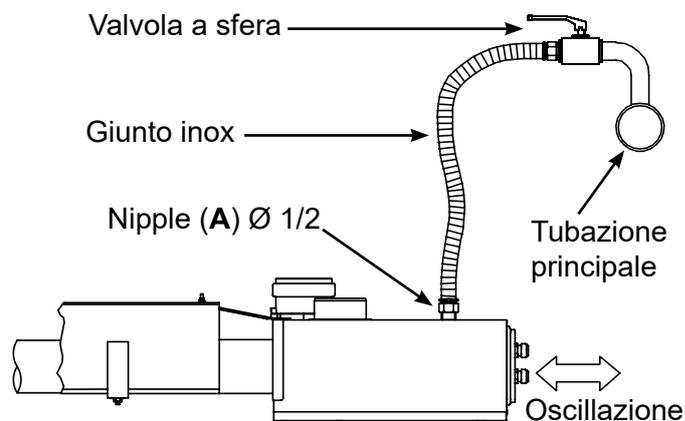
Collegamento alla tubazione principale con giunto inox flessibile (lunghezza minima 30 cm)
